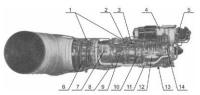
Двигатель ТВ2-117A (вид справа):
